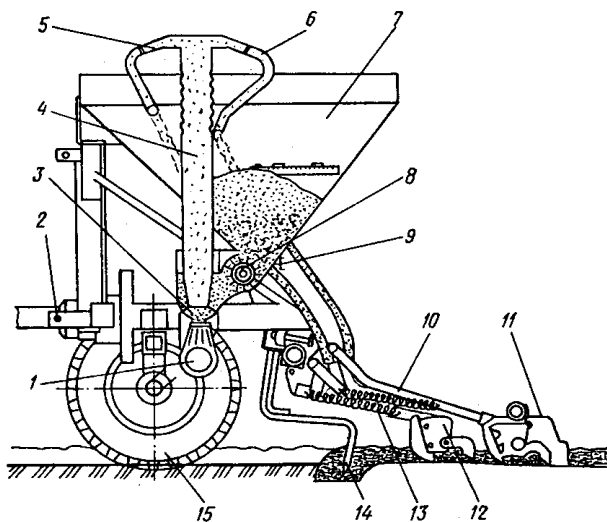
Схема пневматической сеялки объемного высева: 1 – вентилятор; 2 – навеска; 3 – эжекторный питатель; 4 – вертикальный трубопровод; 5 – распределитель; 6 – семяпроводы; 7 – семенной ящик; 8 – катушечный дозатор; 9 – регулятор нормы высева; 10 – поводок; 11 – загорточ; 12 – сошник; 13 – пружина; 14 – рыхлитель; 15 – опорное колесо
